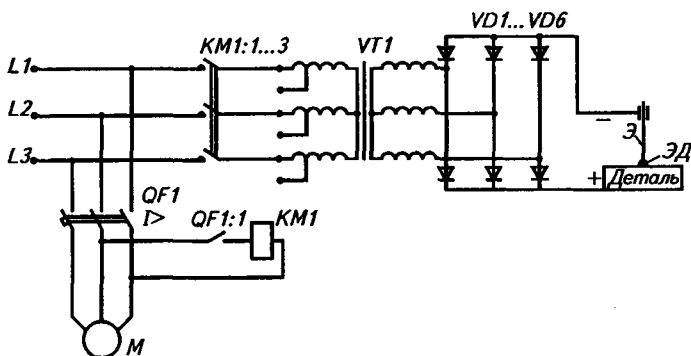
Типовая электрическая схема сварочного выпрямителя
